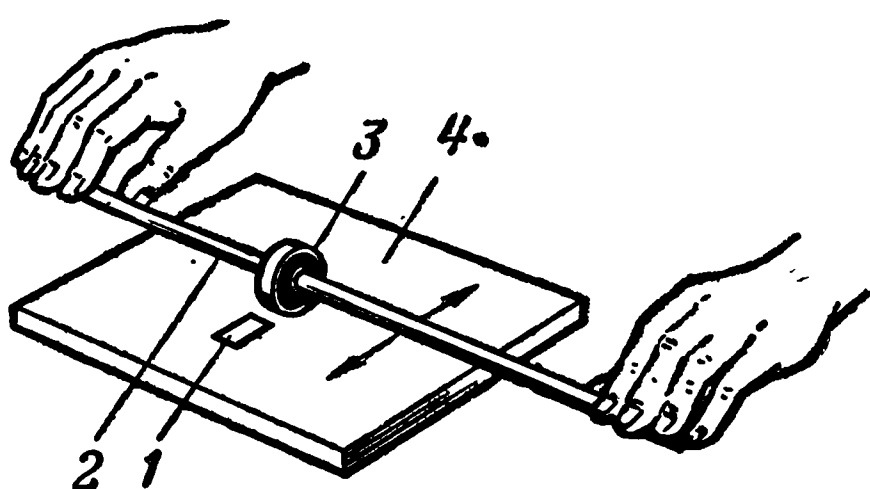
Изготовление прокладки рабочего зазора универсальной головки.
